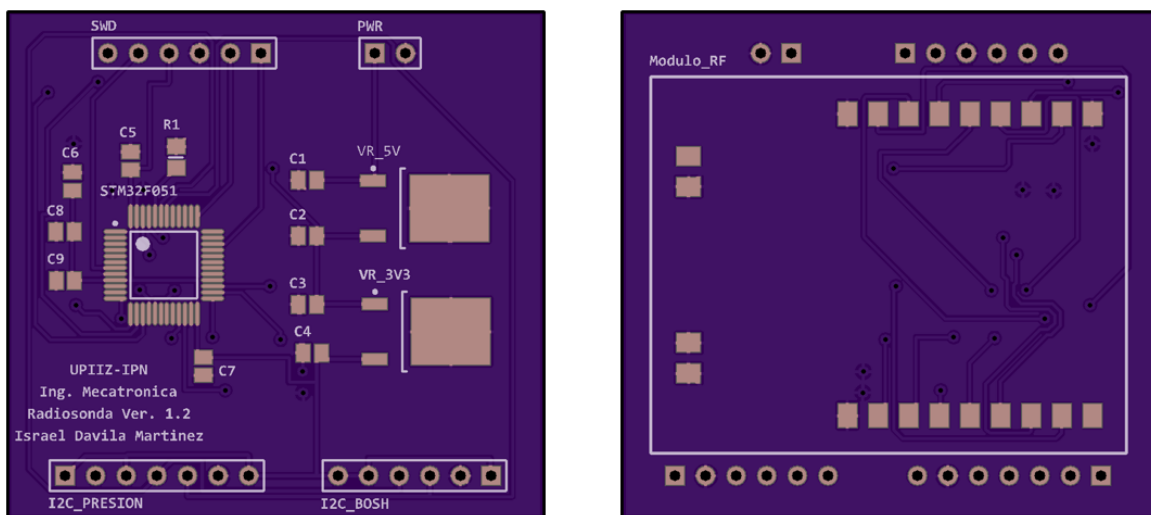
Vista superior (izquierda) e inferior (derecha) de la PCB para la radiosonda.
